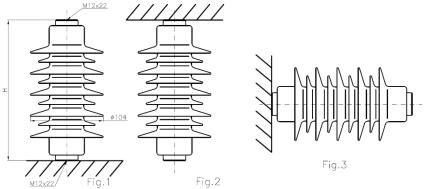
Installationsarten & Lagen Typ PROXAR-IN AC
